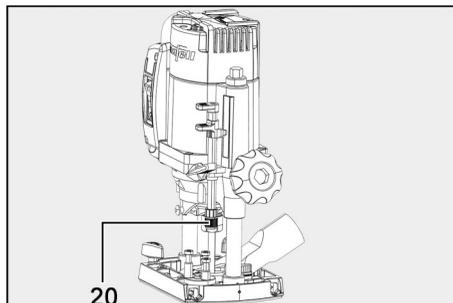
Ajuste fino de la profundidad de fresado en la tuerca de ajuste
